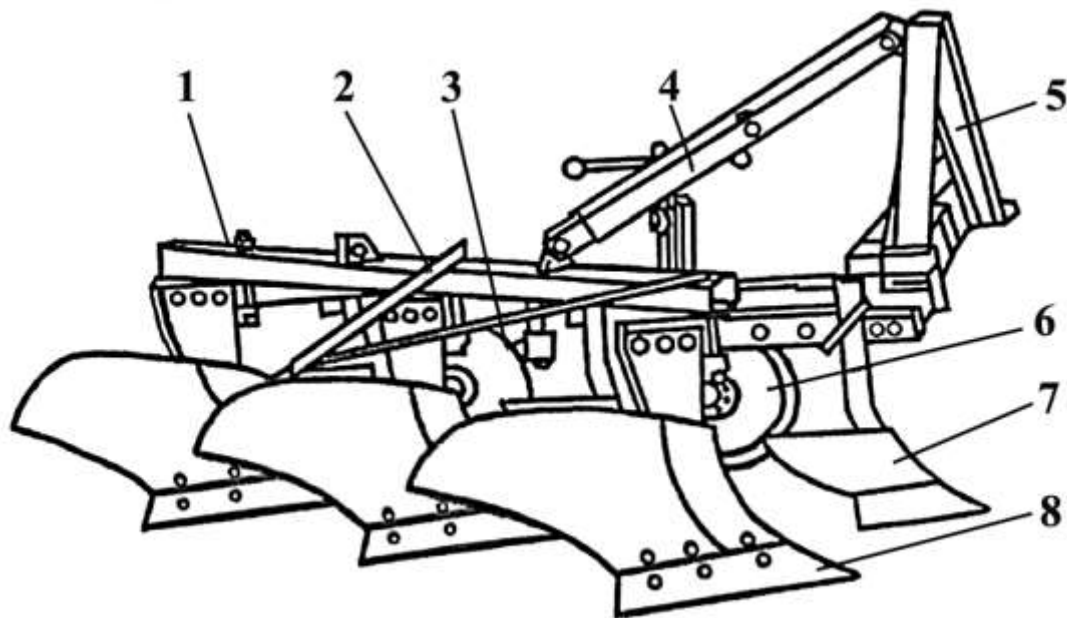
Плуг трикорпусний начіпний ПЛН-3-35:
